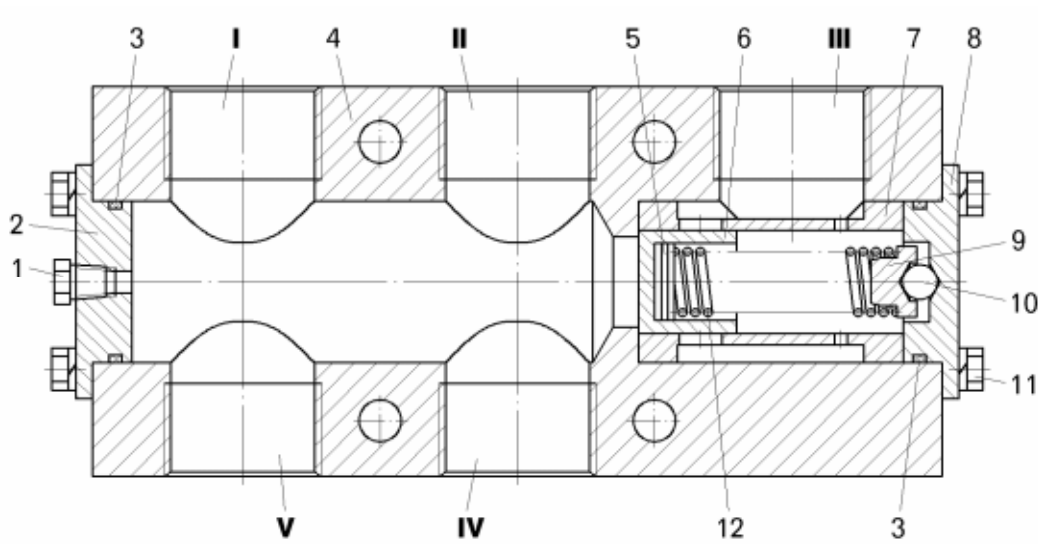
Предохранительный клапан самосвала с многодисковыми маслоохлаждаемыми тормозами:
